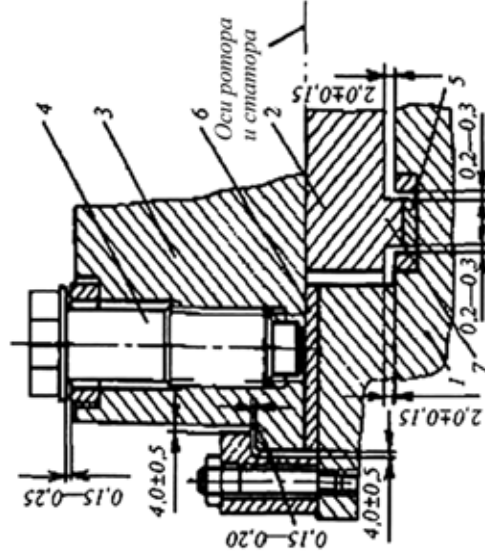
Опираие цилиндров ВД и СД турбин ХТЗ на корпус подшипника: 1 – корпус подшипника; 2 – нижняя лапа; 3 – верхняя лапа; 4 – домкратный болт; 5 – технологическая прокладка; 6 – подгоночная прокладка; 7 – поперечная шпонка
